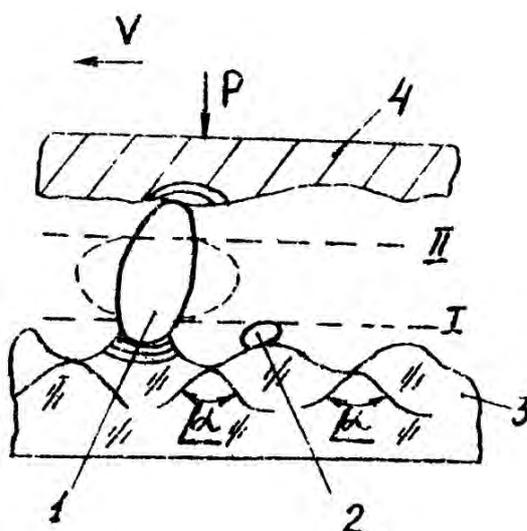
Схема взаимодействия инструмента, абразива и заготовки при шлифовании стекла свободным абразивом
